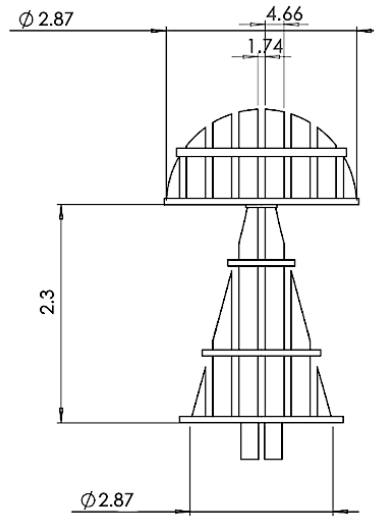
Dibujo técnico en SolidWorks de las dimensiones del lente.
